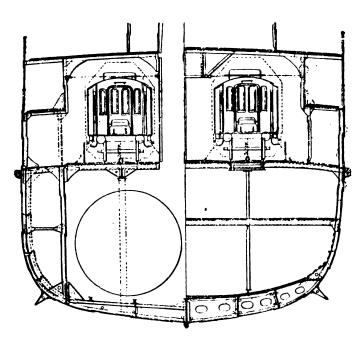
Ferry-boat delle Ferrovie Svedesi - Sezione trasversale.
